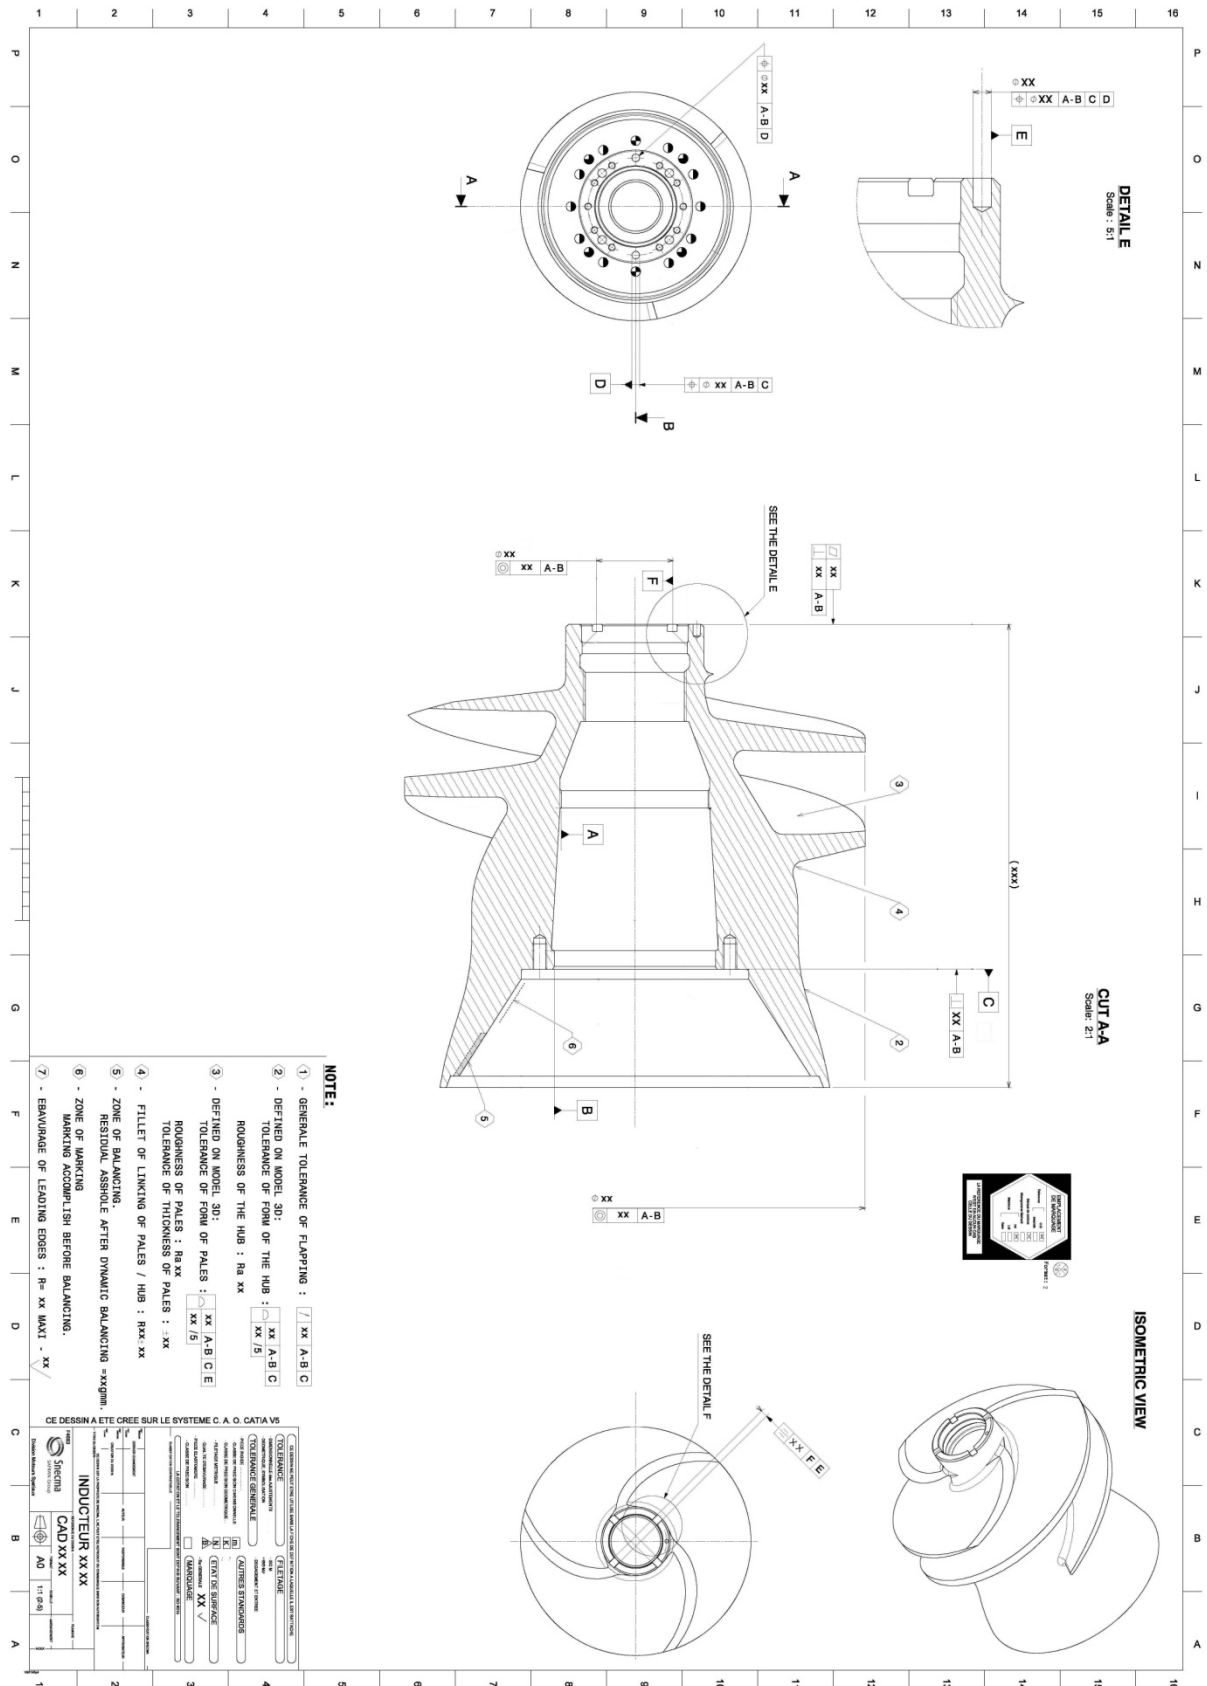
Dessin de définition d'un impeller (source SNECMA).
